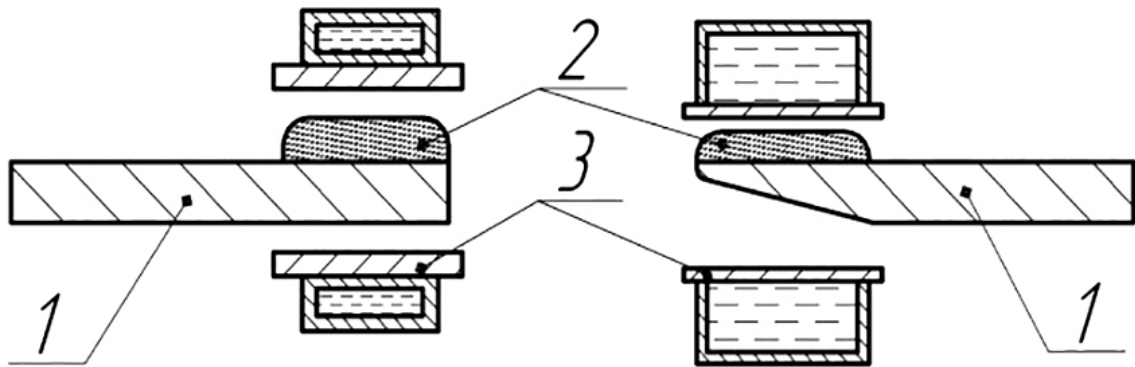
Схема наплавлення деталей, що мають у поперечному перерізі форму пластини клину: 1 – деталь; 2 – шихта; 3 – індуктор.
